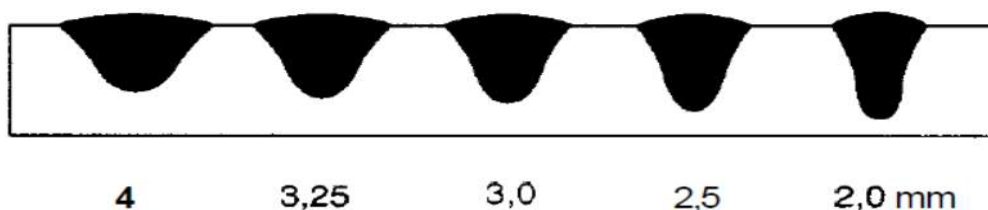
Efectos del cambio de diámetro del aporte en la geometría del cordón de soldadura (8).
